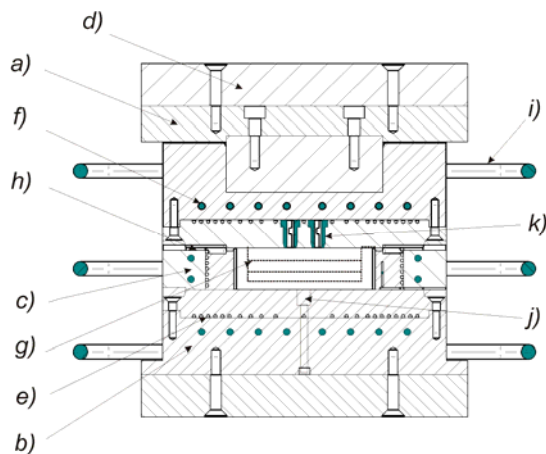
Dessin technique du moule pilote. e) : résistances chauffantes ; f) circuits de refroidissement ; c) garde isolante ; g) pièce
